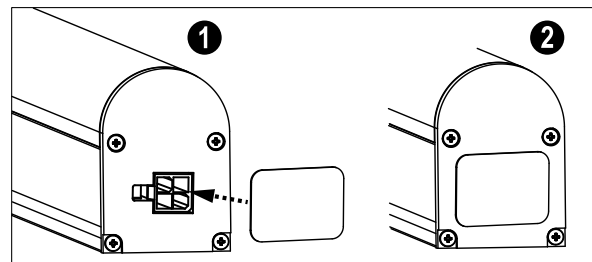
Instalación de cubierta en cascada (Paso 8)
